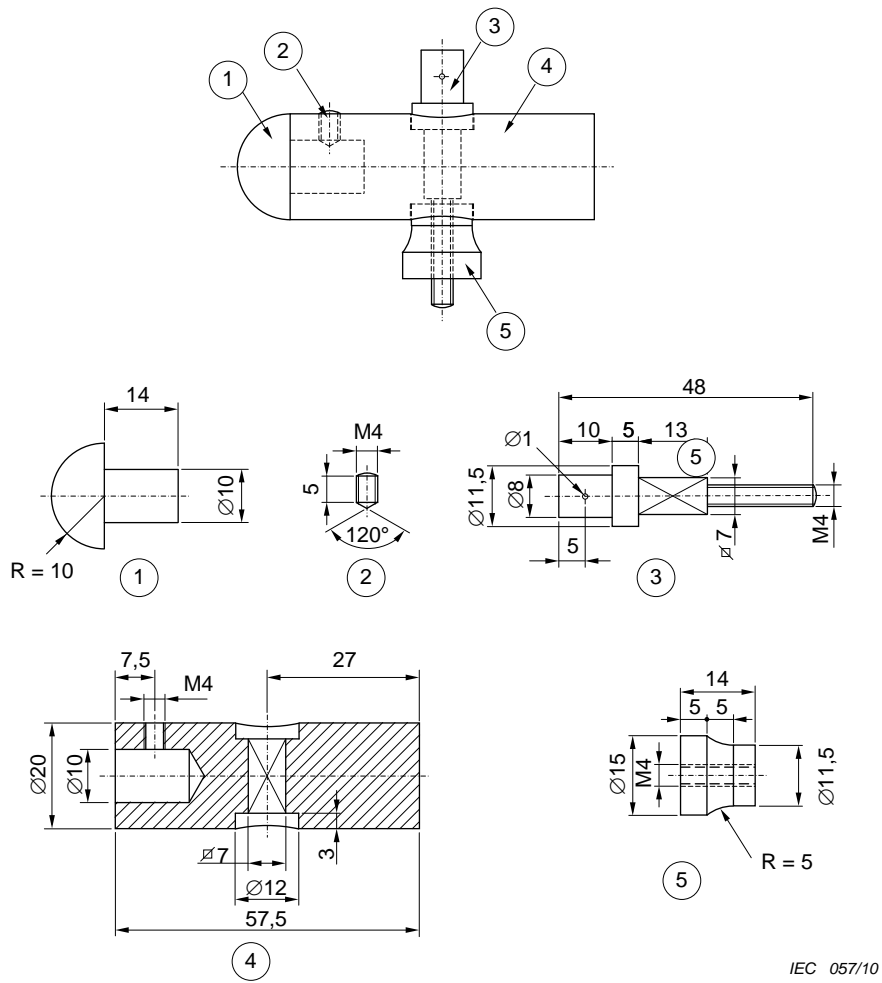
Appareil pour l'essai aux secousses (9.12.1)
